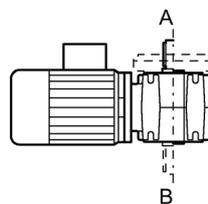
Монтажные позиции для червячного редуктора S, типоразмер 09 - 29
